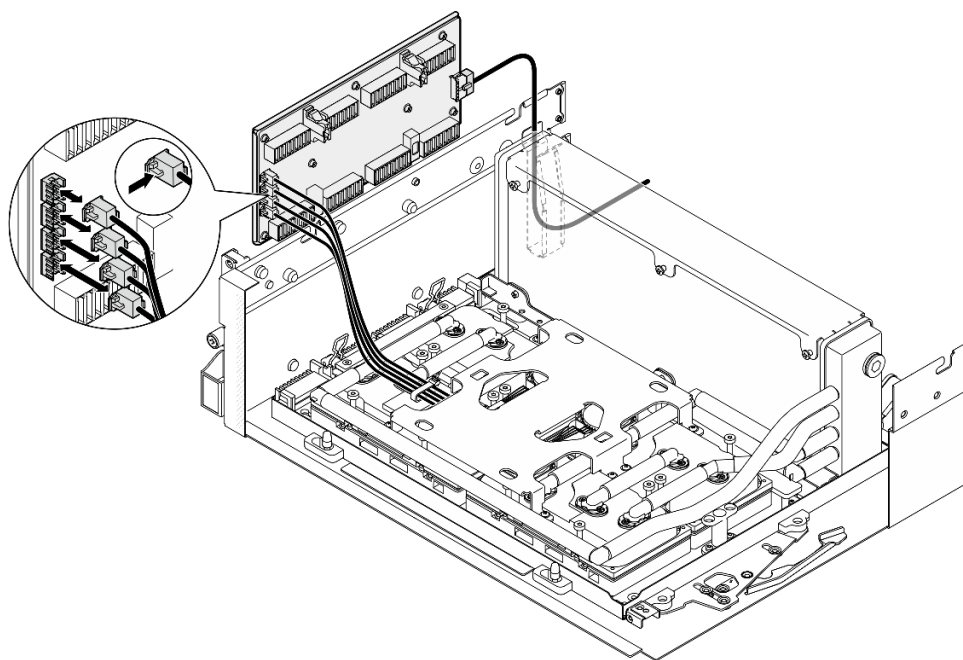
Desconexión del cable de la bomba del conjunto de la placa de frío
